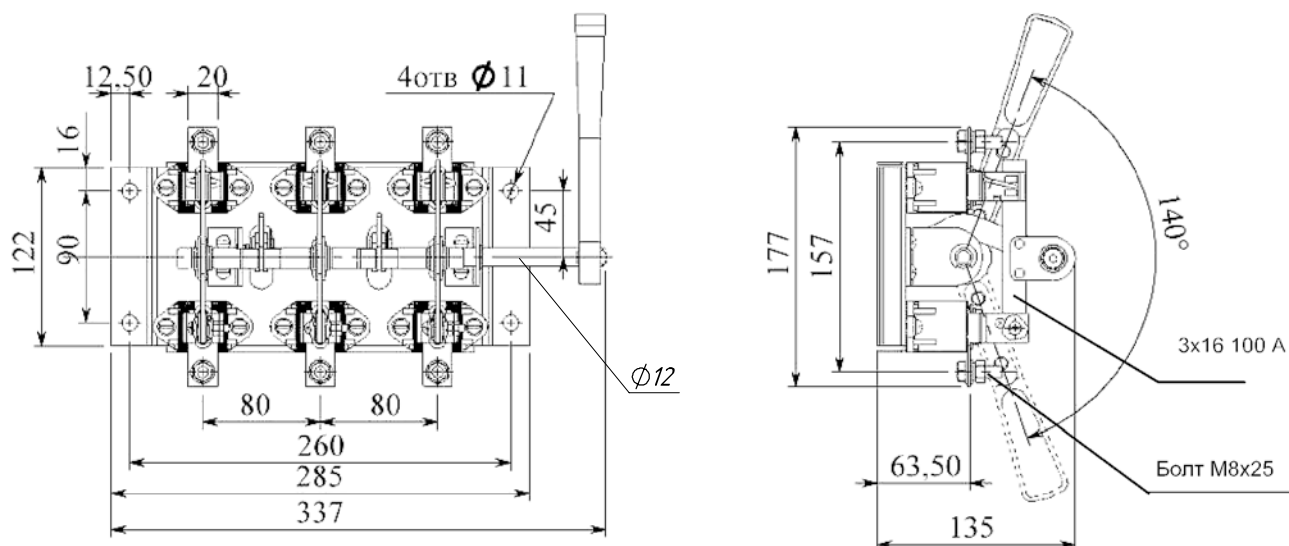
Разъединитель PE19-31-31120-00 УХЛЗ с боковой ручкой
